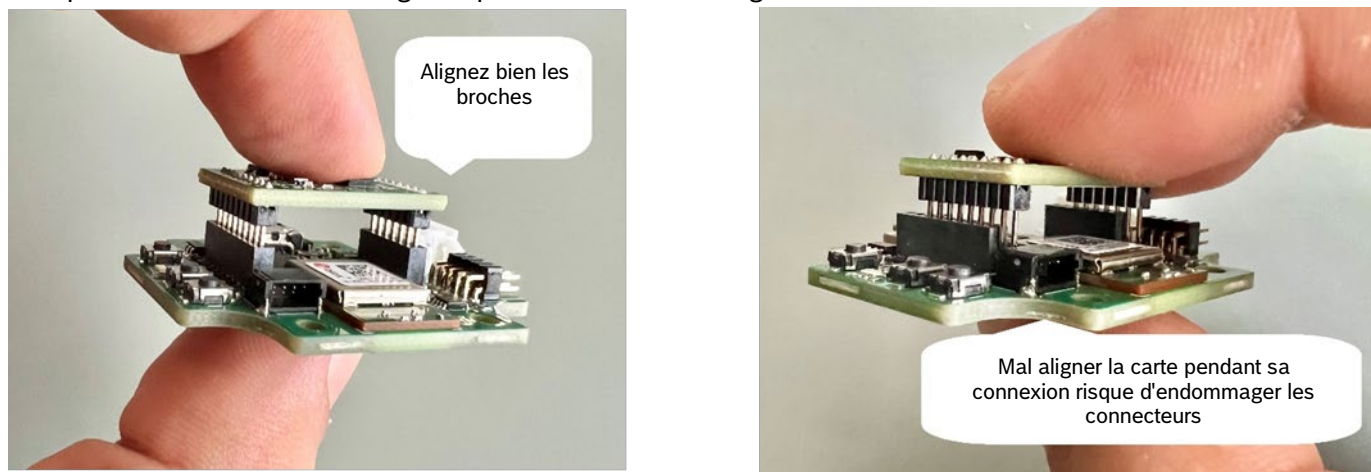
Alignement des broches de la carte Shuttle Board 3.0
